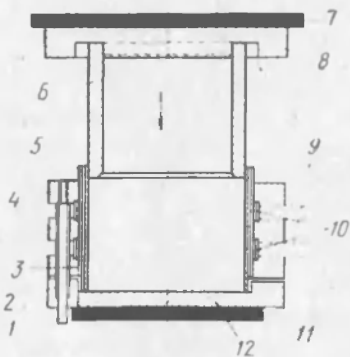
Посадка контактных колец на втулку холодной прессовкой:
